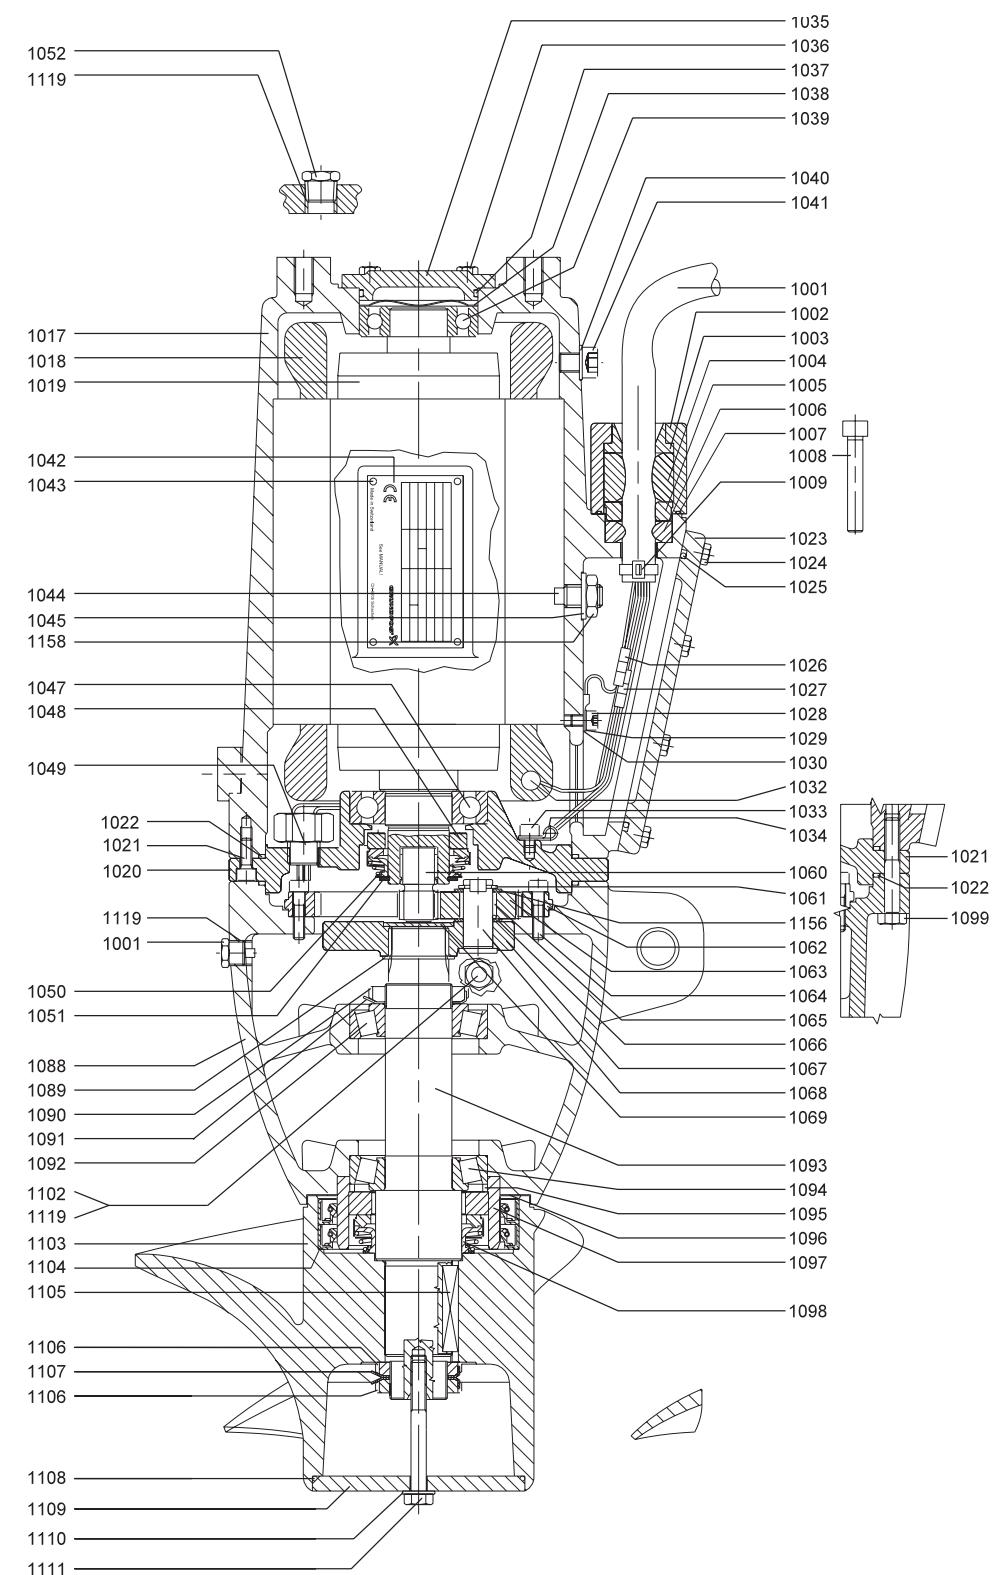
Чертёж в разрезе, SRP.xx.30.xx
